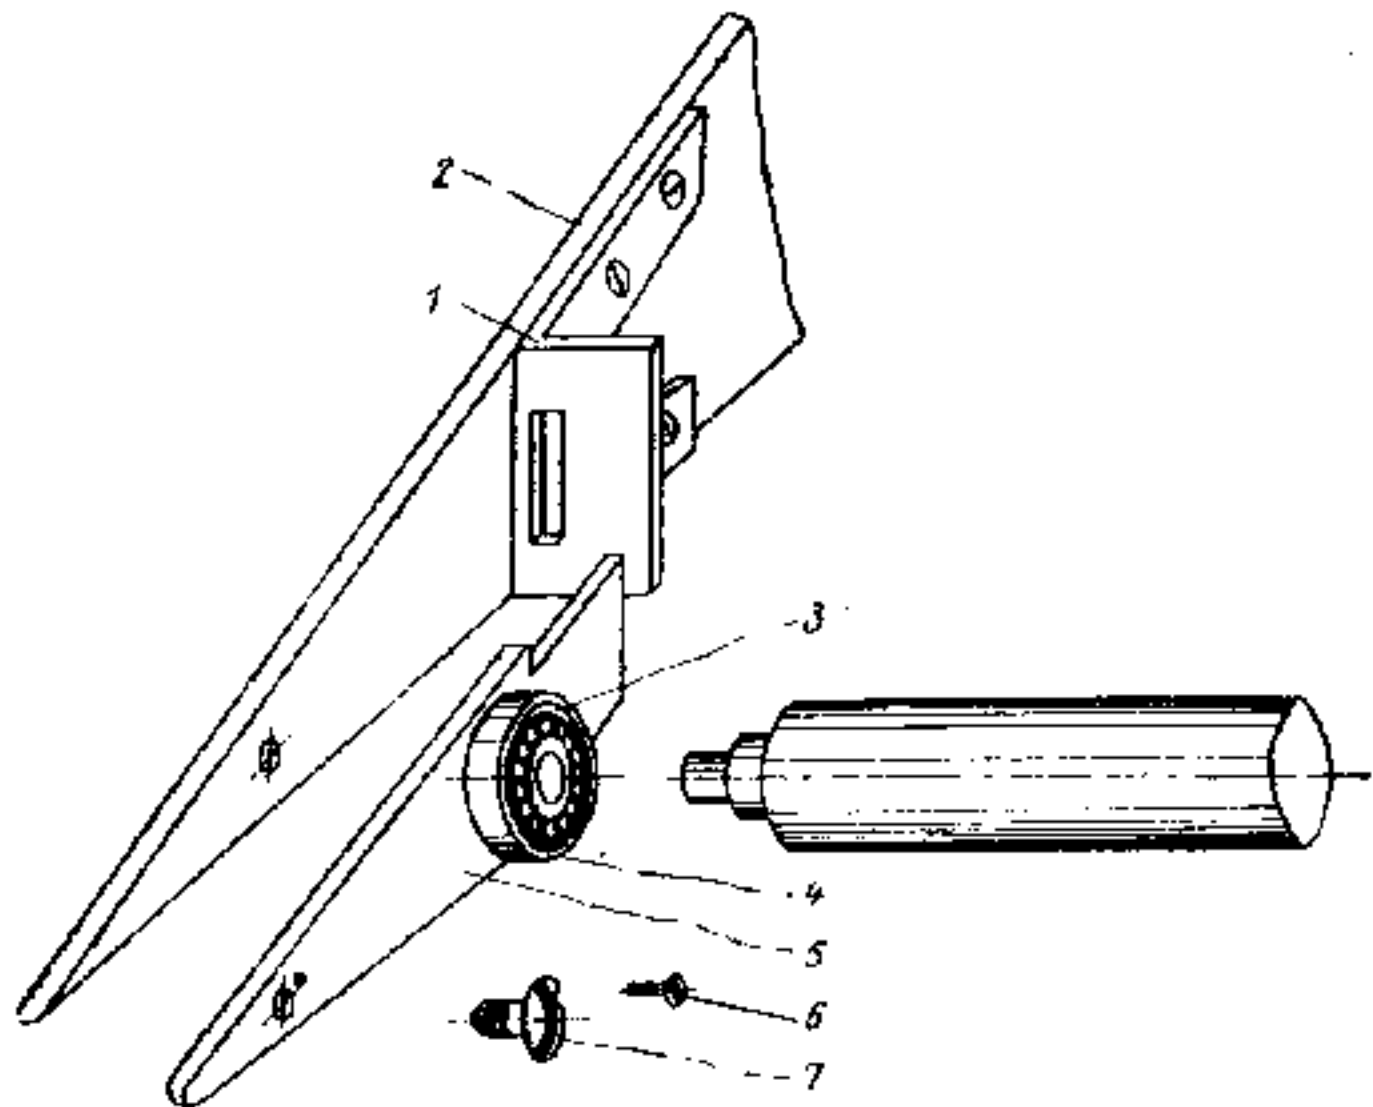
Быстроразъемные узлы крепления рулевых поверхностей.
